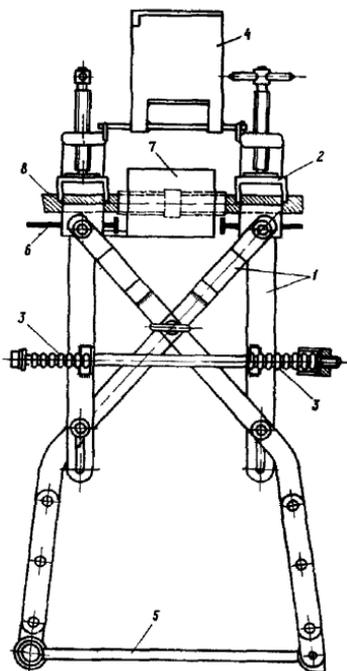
Сварочное приспособление типа ПСП:
